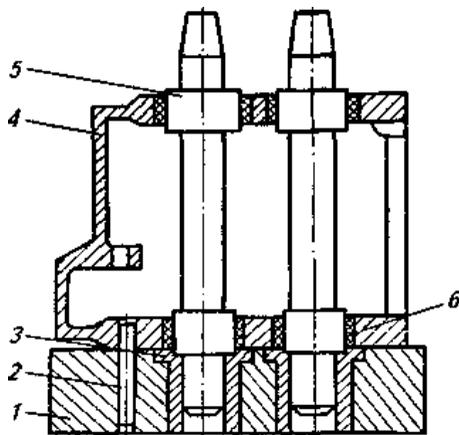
Схема формовки посадочных мест подшипников корпуса коробки передач:
